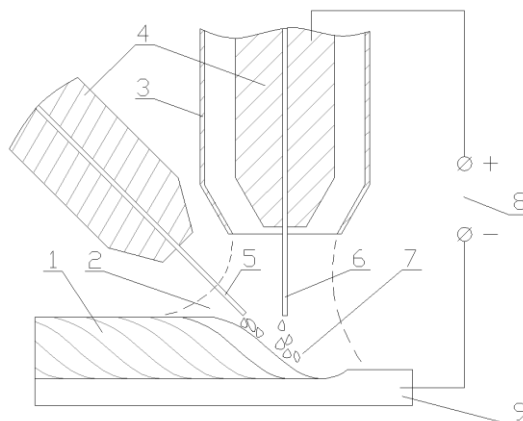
Схема процесса сварки в защитных газах с ДПП:
